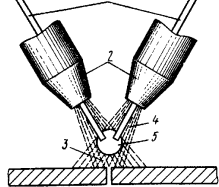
Схема процесса атомно-водородной сварки:
